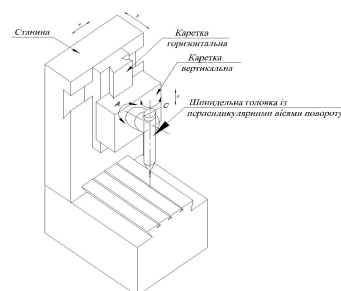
Безконсольний вертикально-фрезерний верстат із поворотною головкою та перпендикулярними вісями повороту головки і шпинделя
